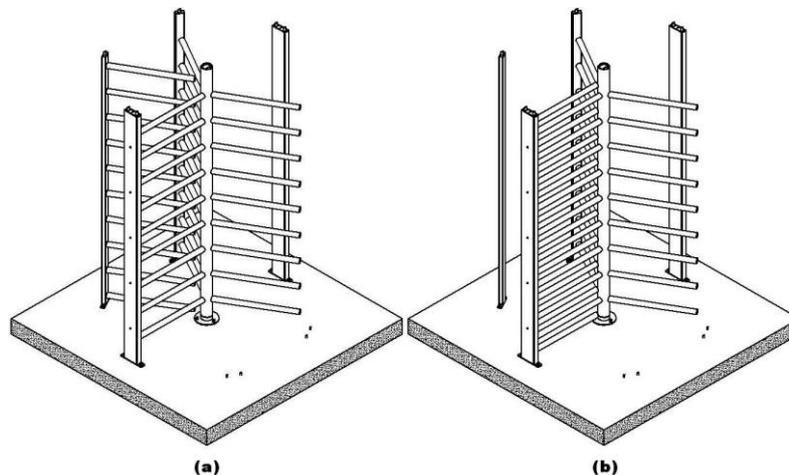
Montagem do braço: (a) Torniquete de 2 Pentes; (b) Torniquete de 1 Pente
